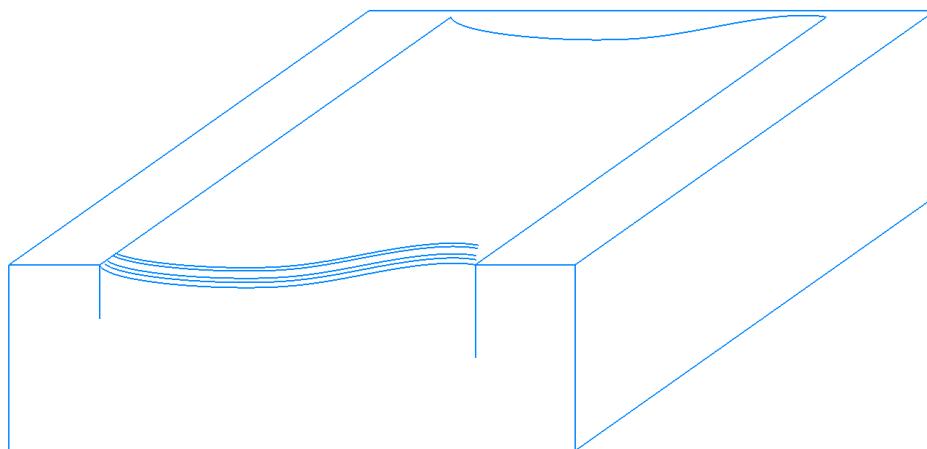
Принципова схема виготовлення верхньої обшивки.
